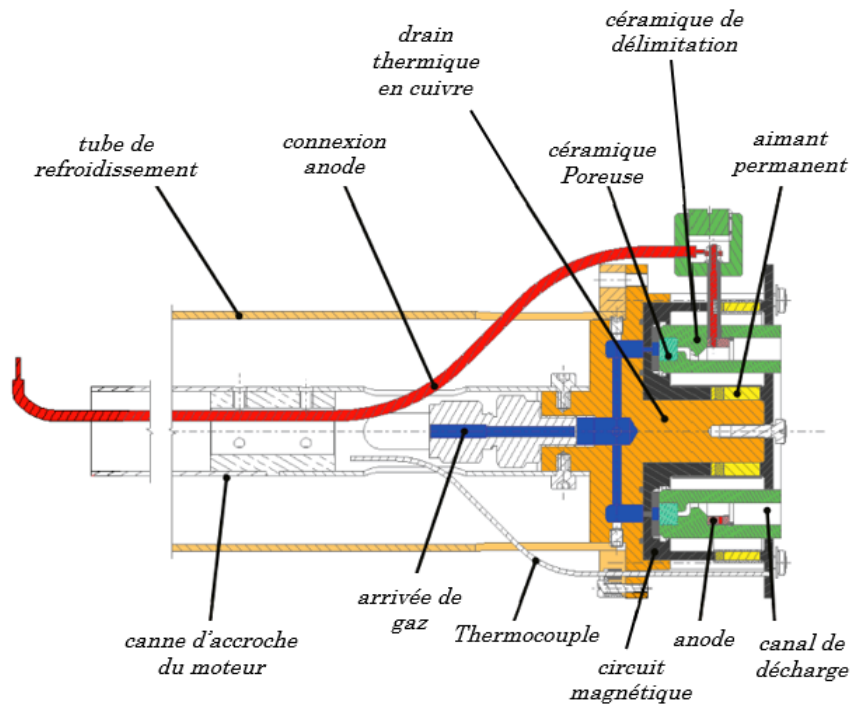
Plan détaillé du PPI250 (vu en coupe) [3]
